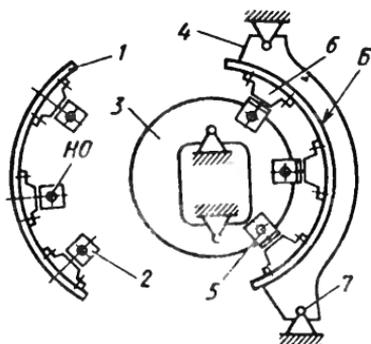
Сборка с базированием по внешней поверхности обшивки:
